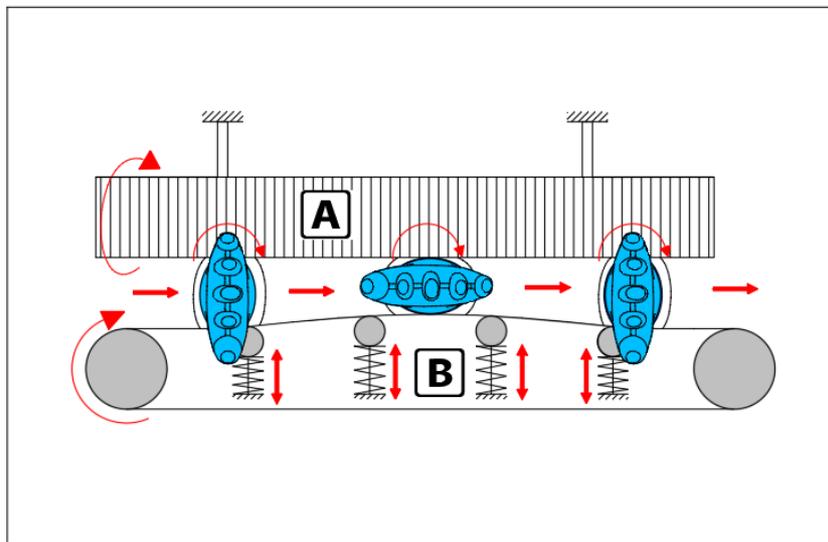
Ilustração da etapa de Beading com elemento de rotação horizontal auxiliado por um mecanismo compensador.
